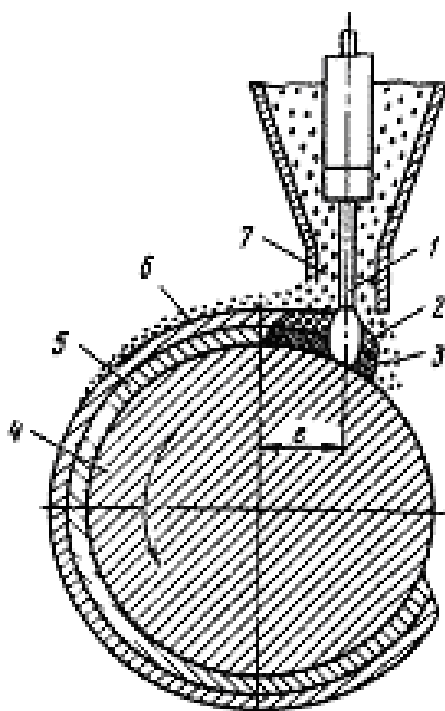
Схема автоматичного наплавлення деталі під флюсом
